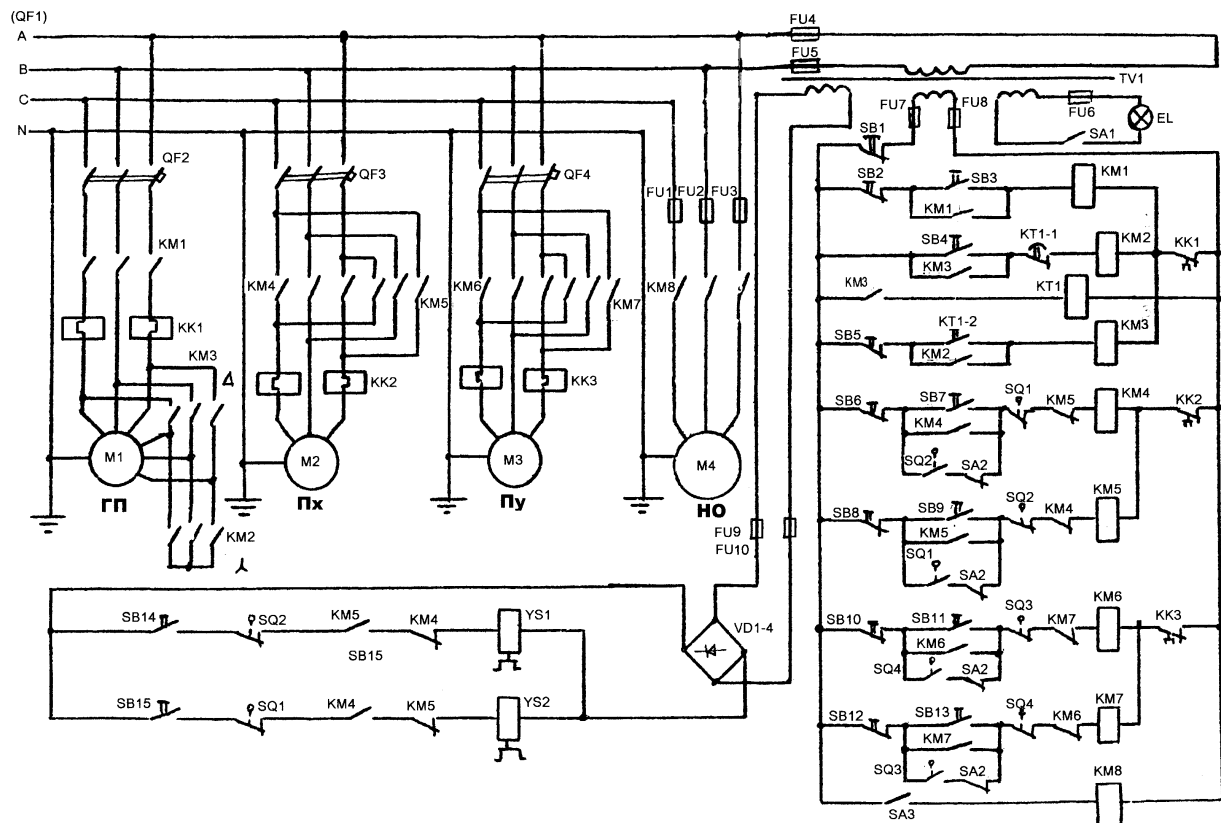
Схема електрична принципова фрезерного верстату 6А59
